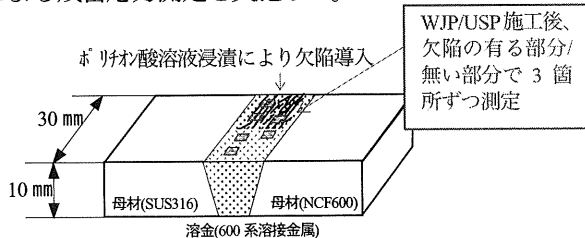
平板試験片形状 (600系溶接金属に欠陥導入した例)
